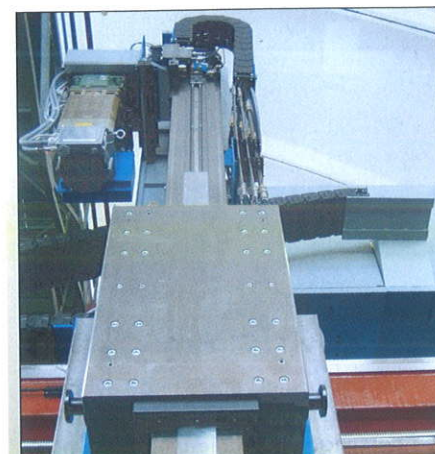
Svislý soustruh s osou Y [TOSHULIN]
